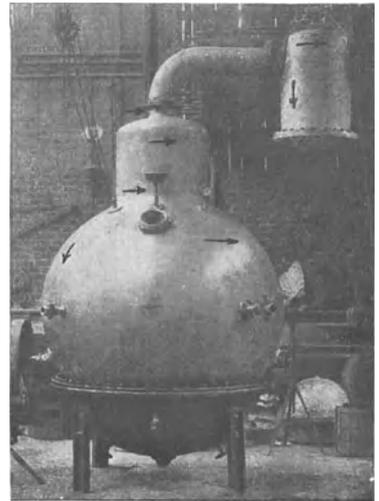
Geschweißter Vakuum-Verdampfapparat.
